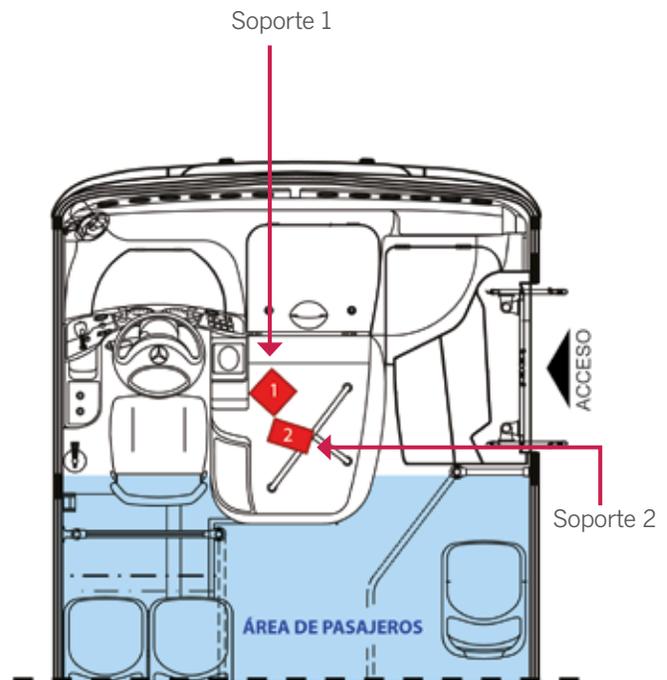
Vista superior de cabina de Boxer. Fuente propia.
